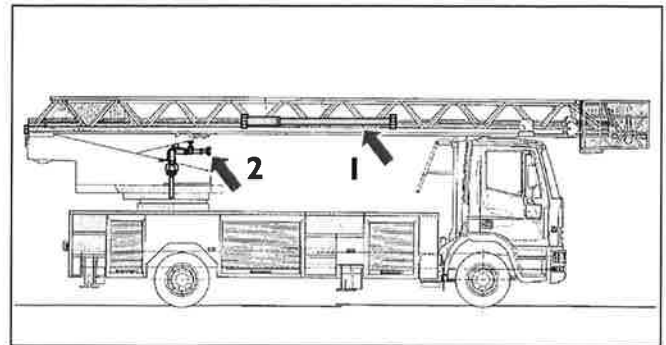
/1 Halterung Schlauchhalter und formfester Druckschlauch (Pos. 1) Halterung Wendestahlrohr (Pos. 2).
